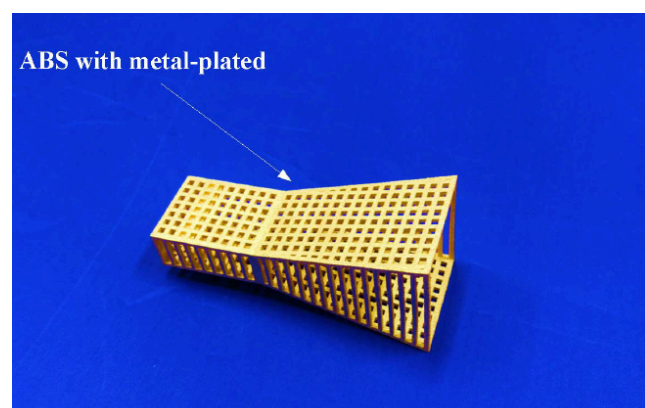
Bocina metalizada a partir de técnica de impresión de polímero [21].
